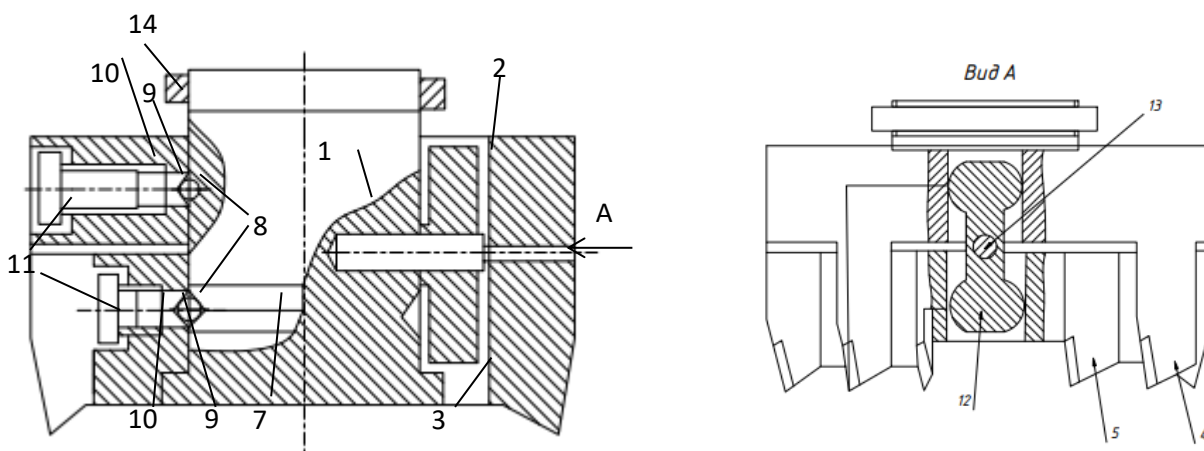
Торцева фреза по а.с. 1053983 МКИ В 23 С 5/06 [3]
